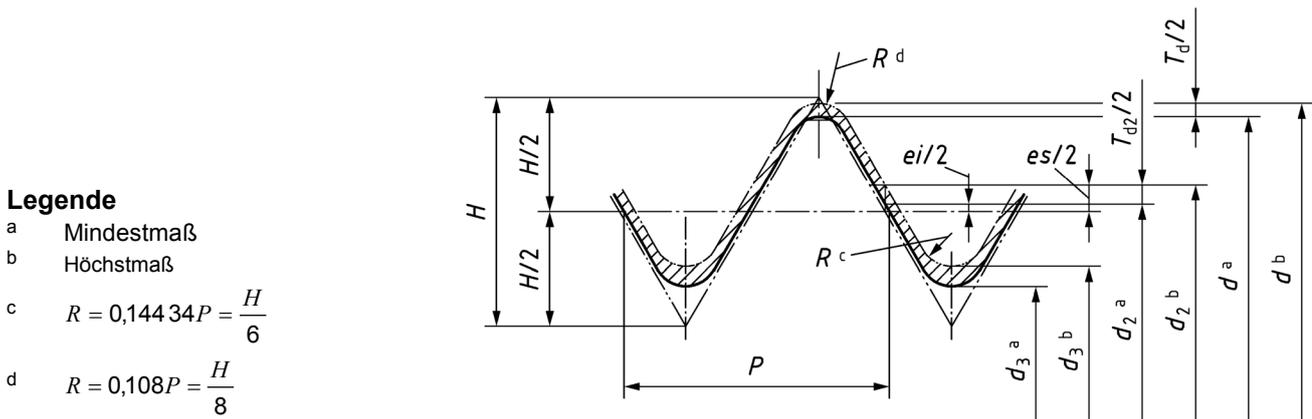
Außengewinde mit positiven Grundabmaßen in Flanken- und Außendurchmesser; Toleranzfeldlage Sn 4 dicht
